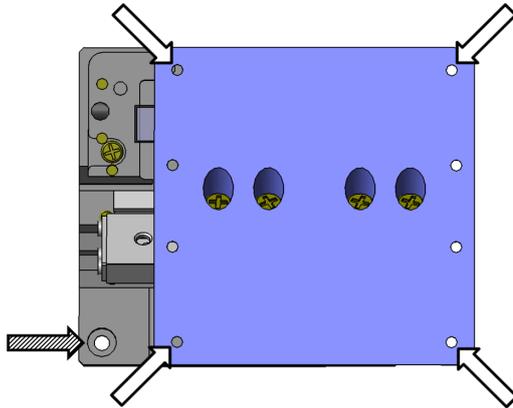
Gewindebohrungen in der Bewegungsplattform für die Montage gestapelter Systeme (weiße Pfeile) und eine von drei Senkbohrungen im Grundkörper des U-521 (schraffierter Pfeil)
